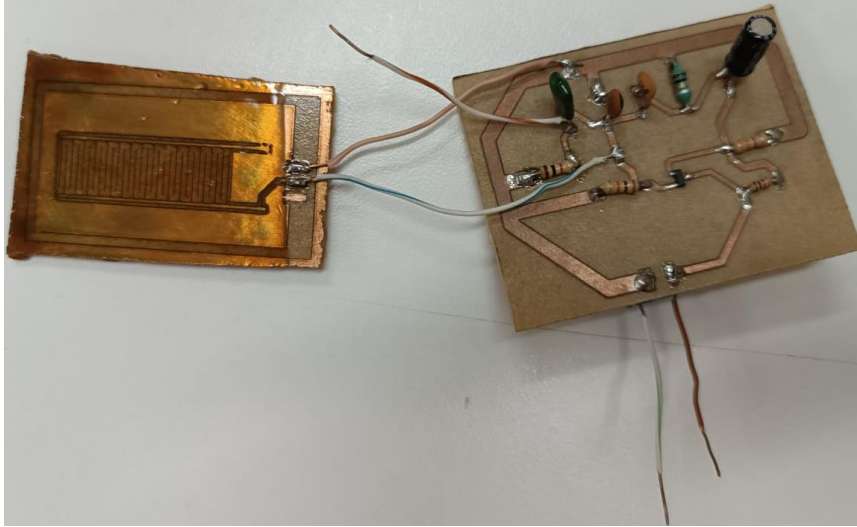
Oscilador Colpitts montado na placa de circuito impresso.
